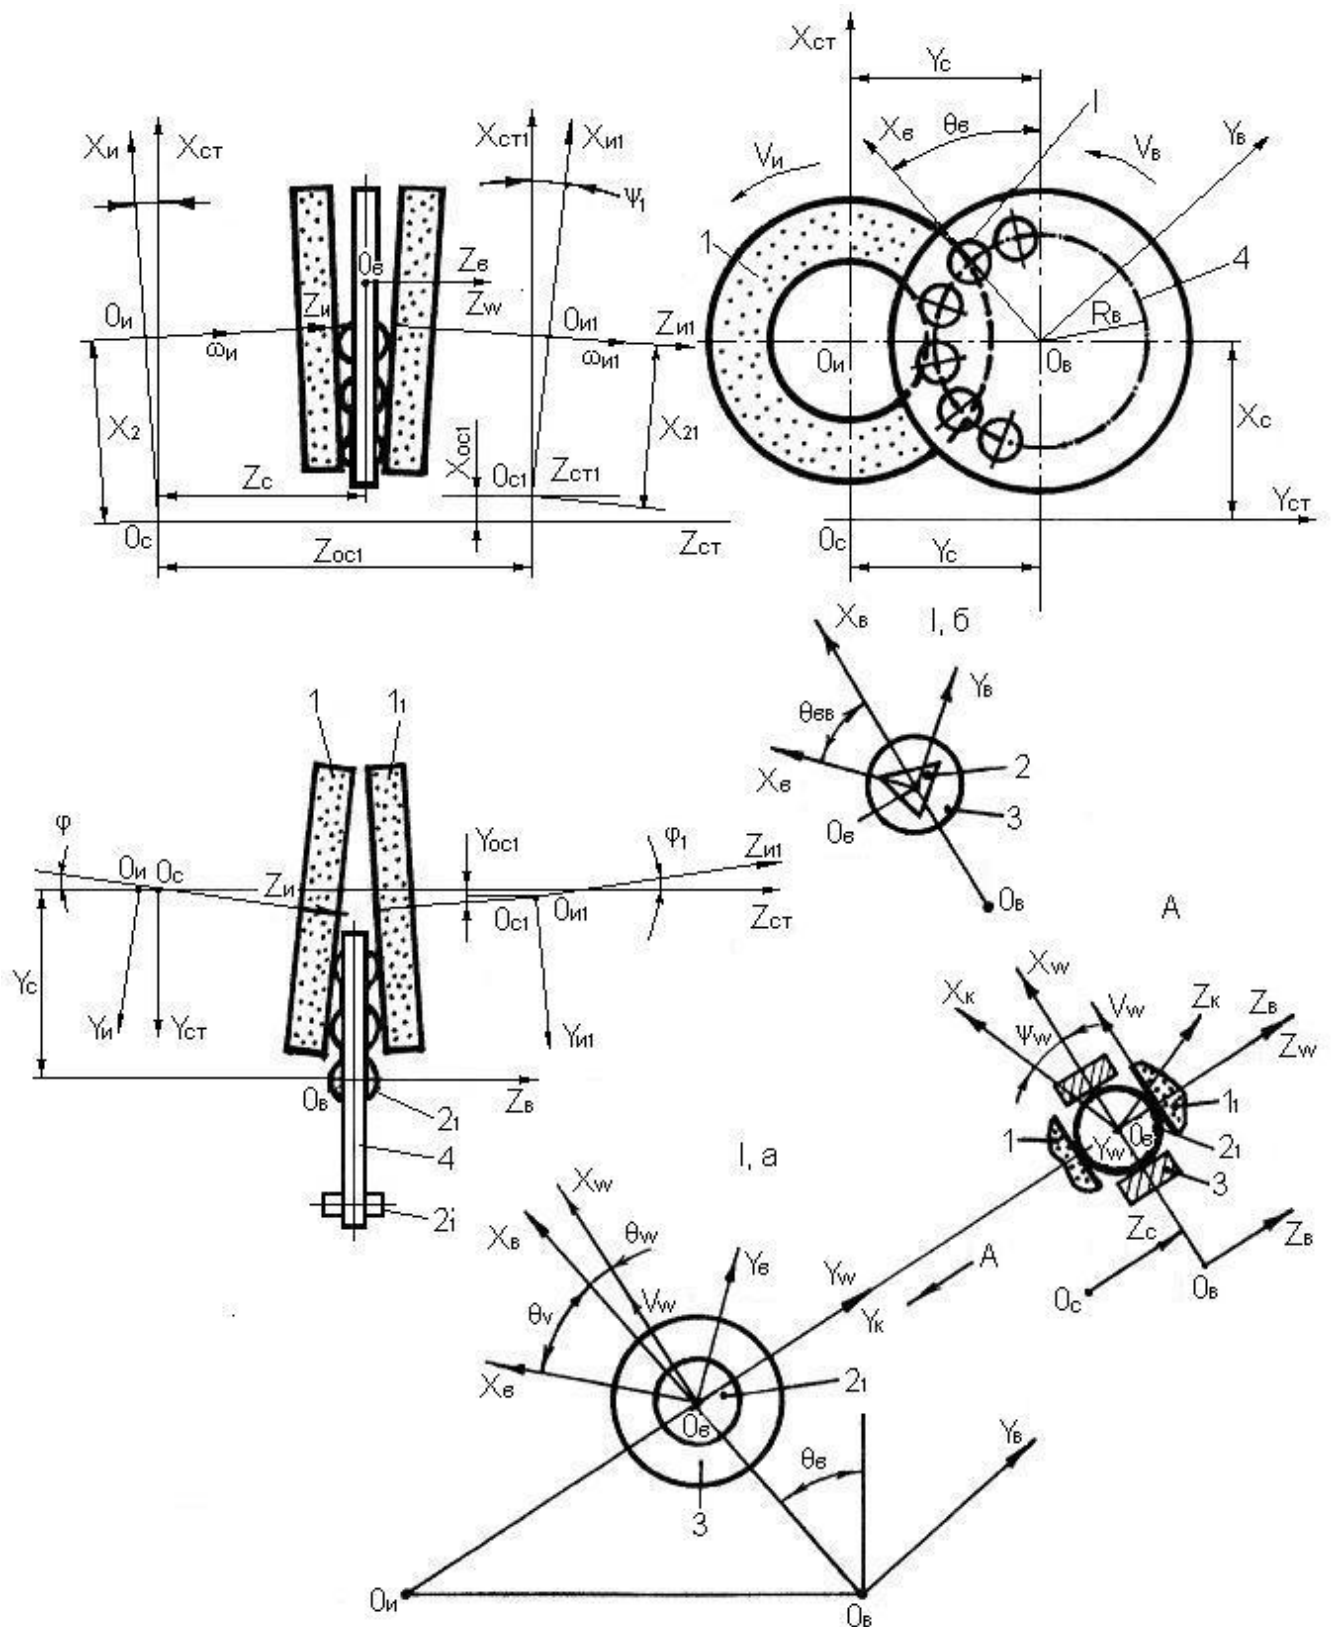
Общая схема формообразующих систем станков для шлифования поверхностей со скрещивающимися осями кругов и деталей
